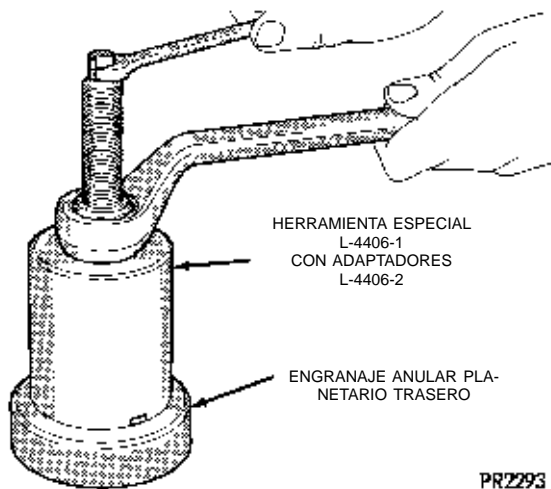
Desmontaje del cono de cojinete del engranaje anular planetario trasero
